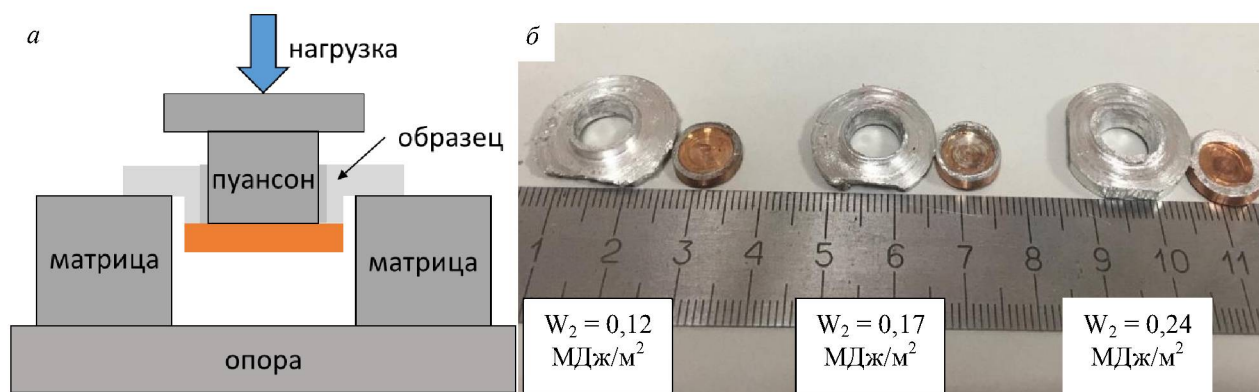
Схема проведения механических испытаний на отрыв слоев биметалла (а) и внешний вид образцов-выдавок после разрушения (б)
